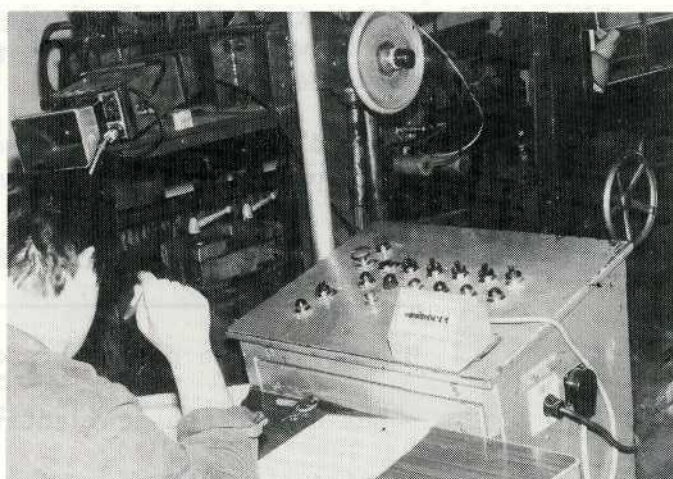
Nazicht van het uitzicht van de spoorstaven na doorgang door de rollenrichtmachine.
